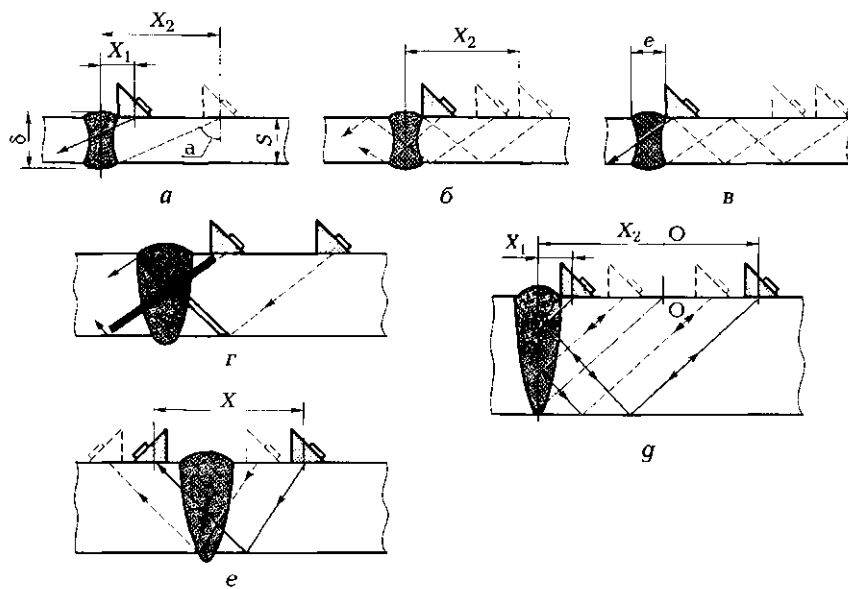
Схемы «прозвучивания» стыковых сварных швов:
